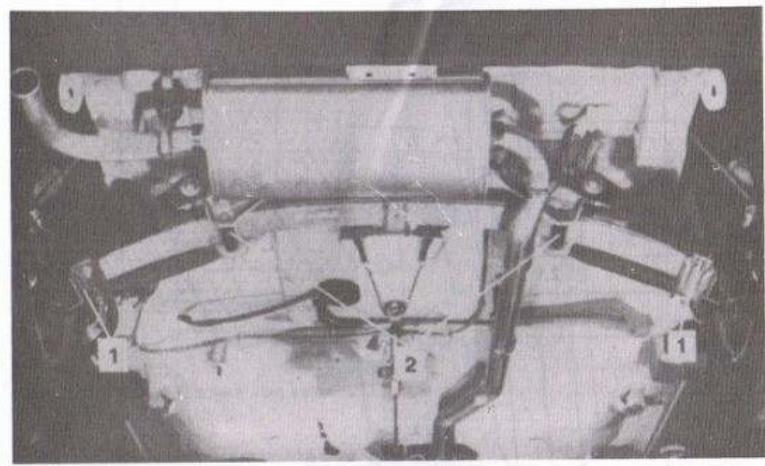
Disposición de montaje y fijaciones de la ballesta
